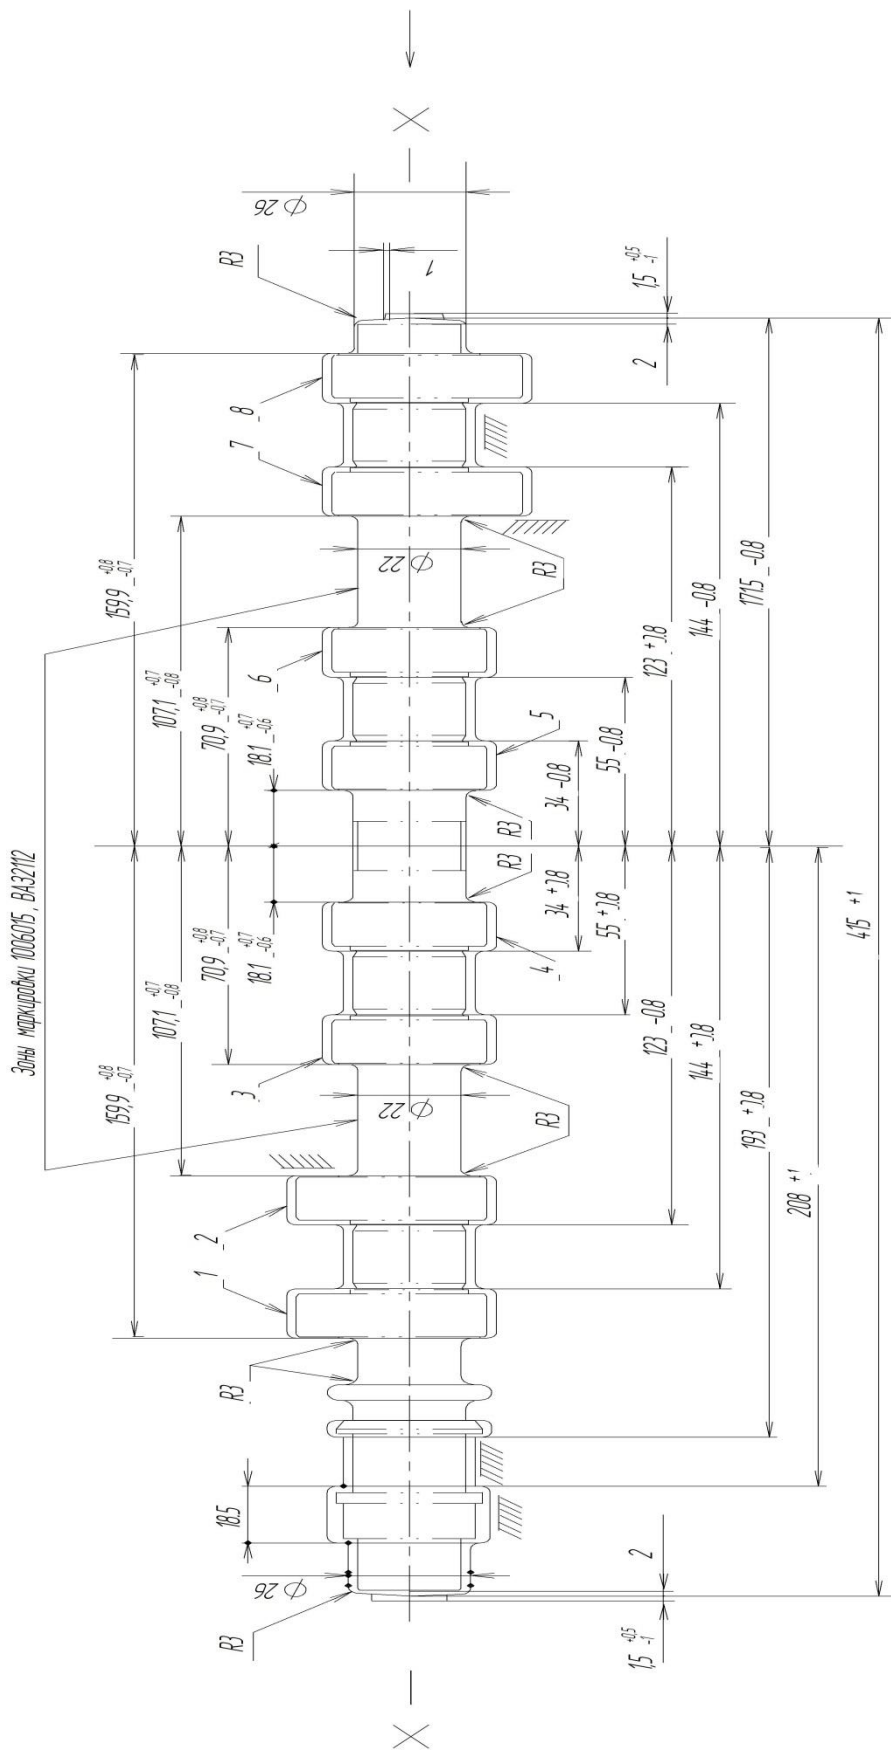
Общий вид заготовки детали - «Распредвал»
